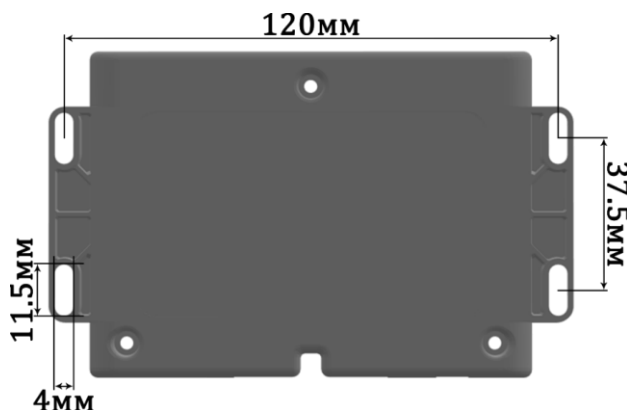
Места крепления корпуса БГ24-АСН-М2
